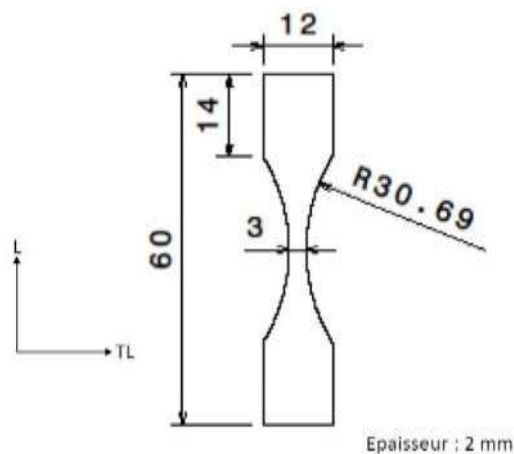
Design et dimensions d'une éprouvette de fatigue
